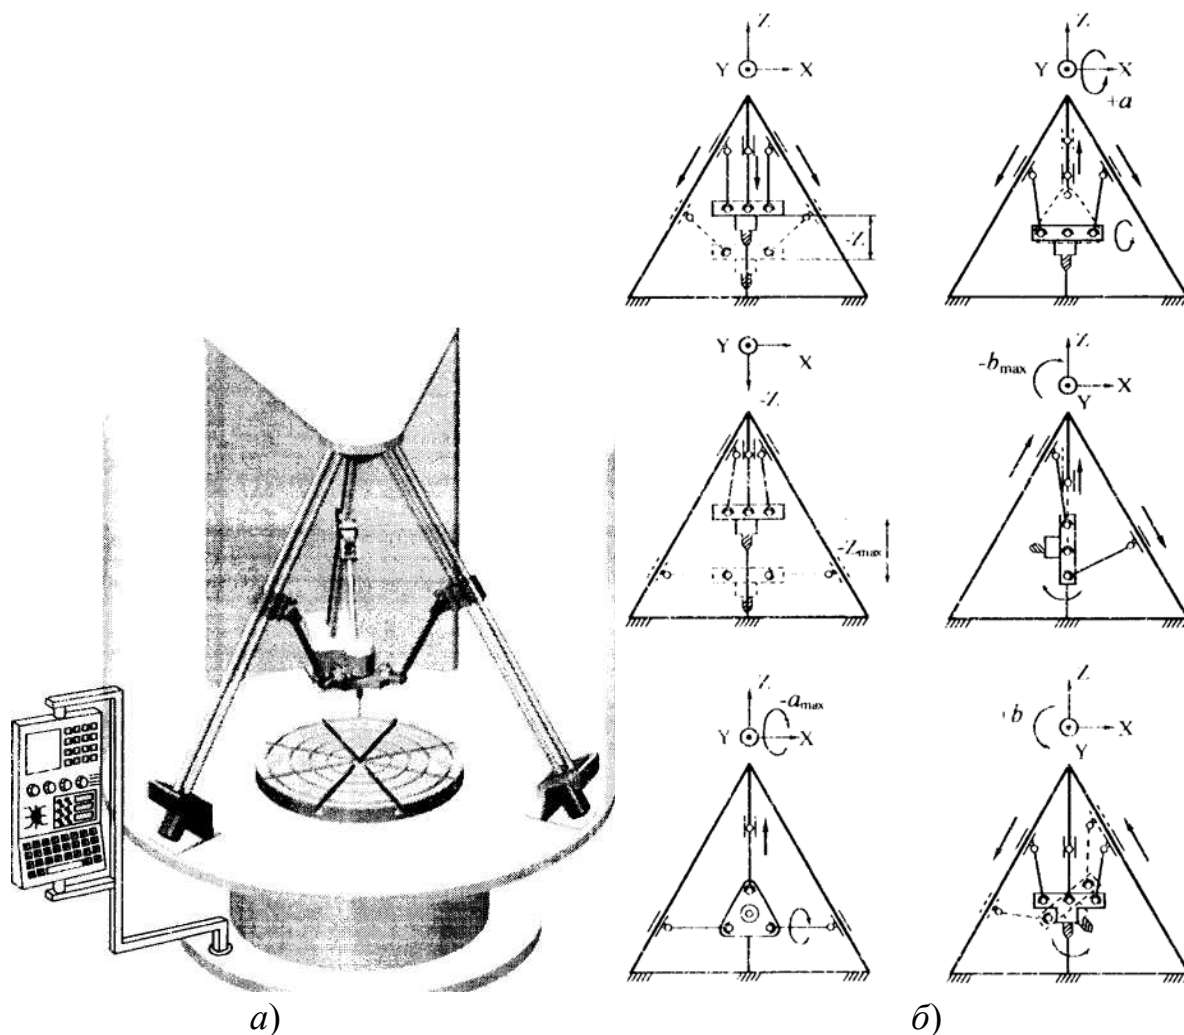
Многокоординатный сверлильно-фрезерный станок повышенной жесткости
